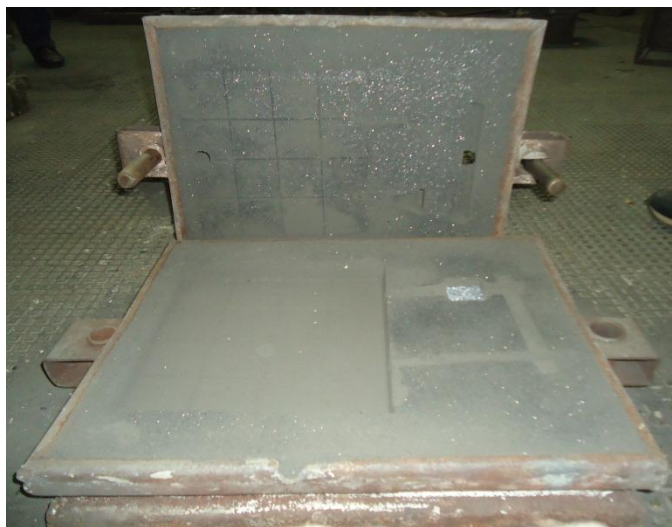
Ливарна форма перед збиранням для виготовлення виливка «Горизонтальна плита»
